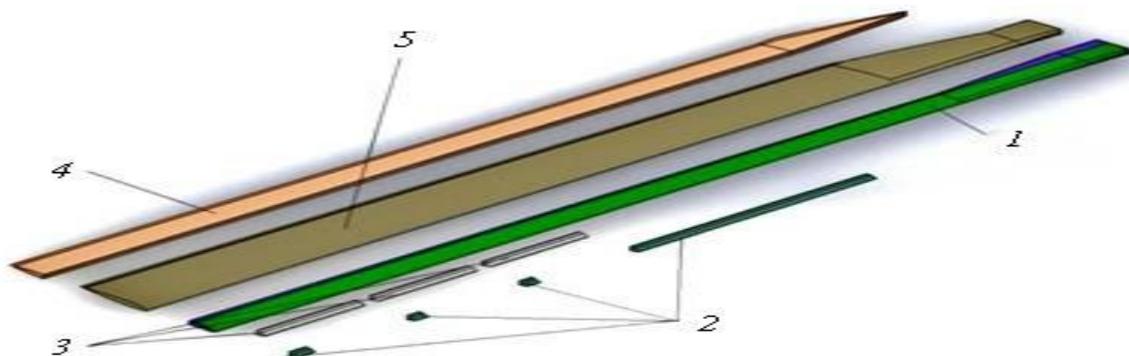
Конструкция лопасти из стеклопластика для БПЛА вертолетного типа: 1 – лонжерон; 2 – наполнитель носка; 3 – свинцовые противофлаттерные грузы; 4 – наполнитель хвостика; 5 – обшивка
